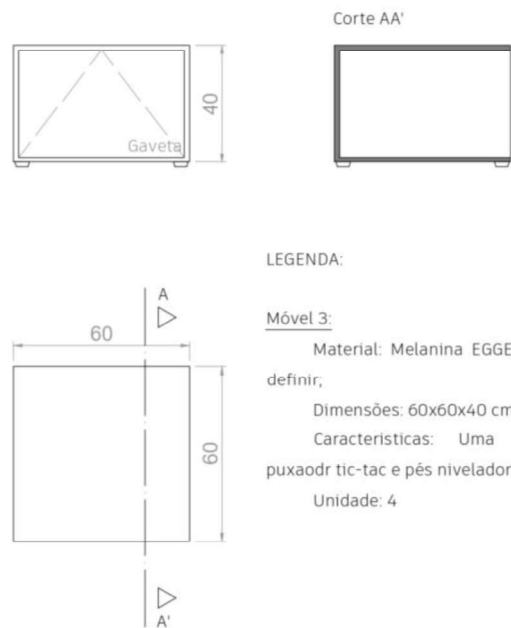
Desenho técnico de produção, módulo 3. Fonte: Autor
